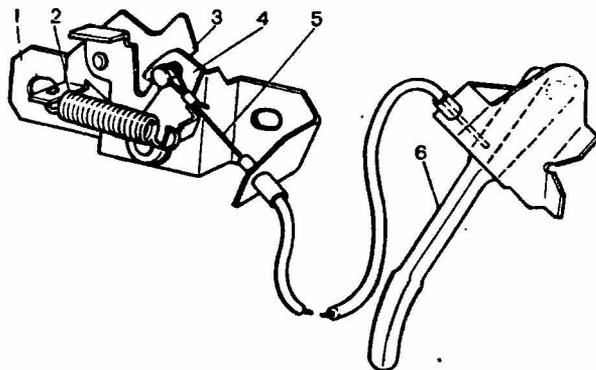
Замок капота: 1 - корпус замка; 2 - пружина; 3 - выталкиватель; 4 - крючок; 5 - тяга привода; 6 - рукоятка привода
